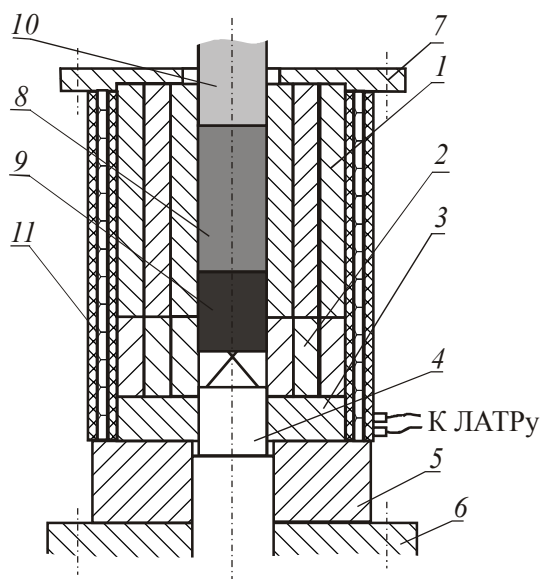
Схема установки для винтовой экструзии: 1 – контейнер, 2 – винтовая матрица, 3 – втулка с профильным каналом, 4 – пуансон противодействия, 5 – опорная плита, 6 – неподвижная траверза прессы, 7 – фланец, 8 – обрабатываемая заготовка, 9 – фальшзаготовка, 10 – пуансон, 11 – нагреватель
